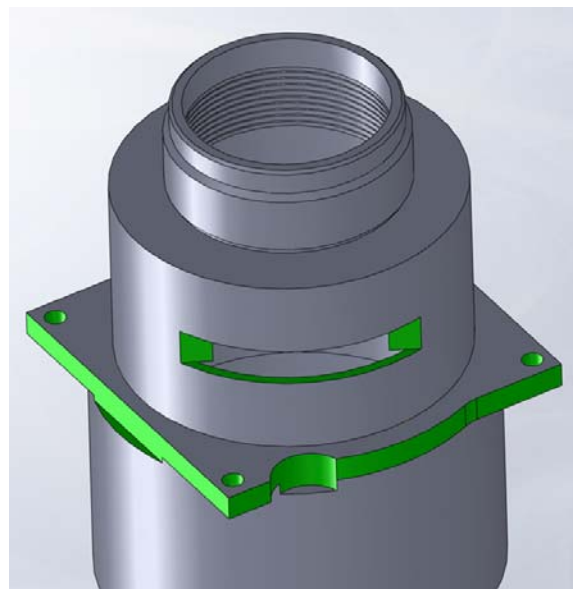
Межоперационная заготовка детали типа «Оправа» с визуально изображенными обрабатываемыми поверхностями многоцелевой операции на станке ЛФ260МФЗ
